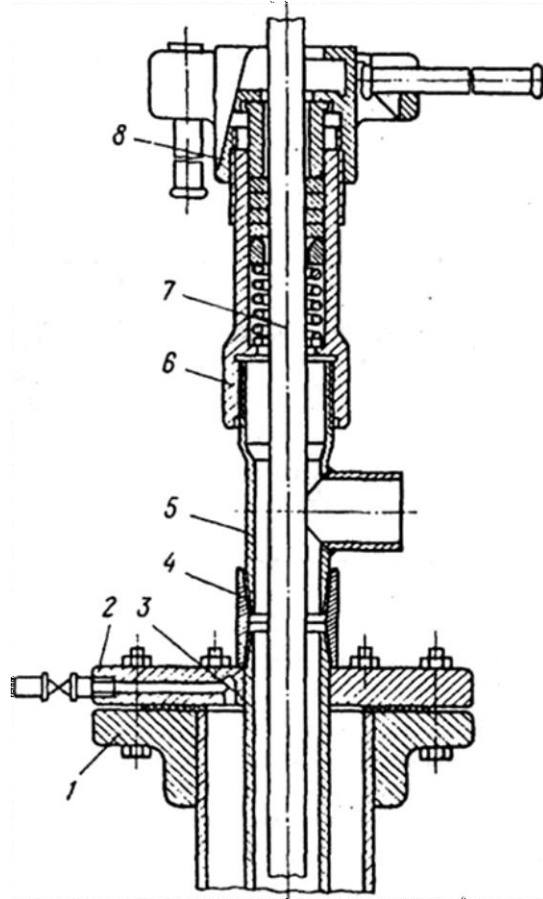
Типове обладнання устя свердловини для штангової насосної установки:
